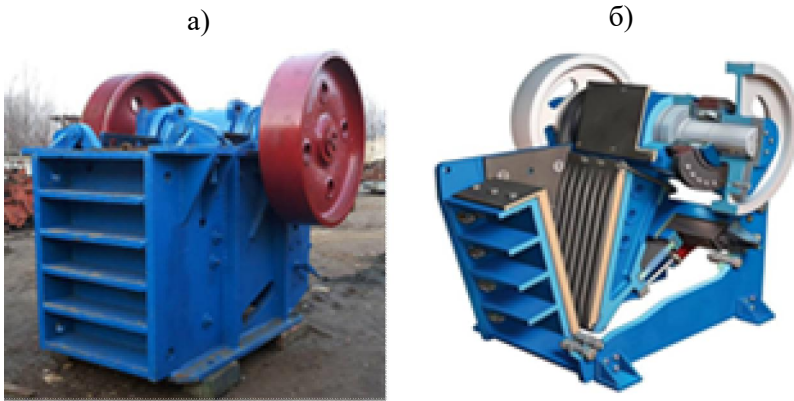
Щоккова дробарка N-МАК з складним рухом щоки:
